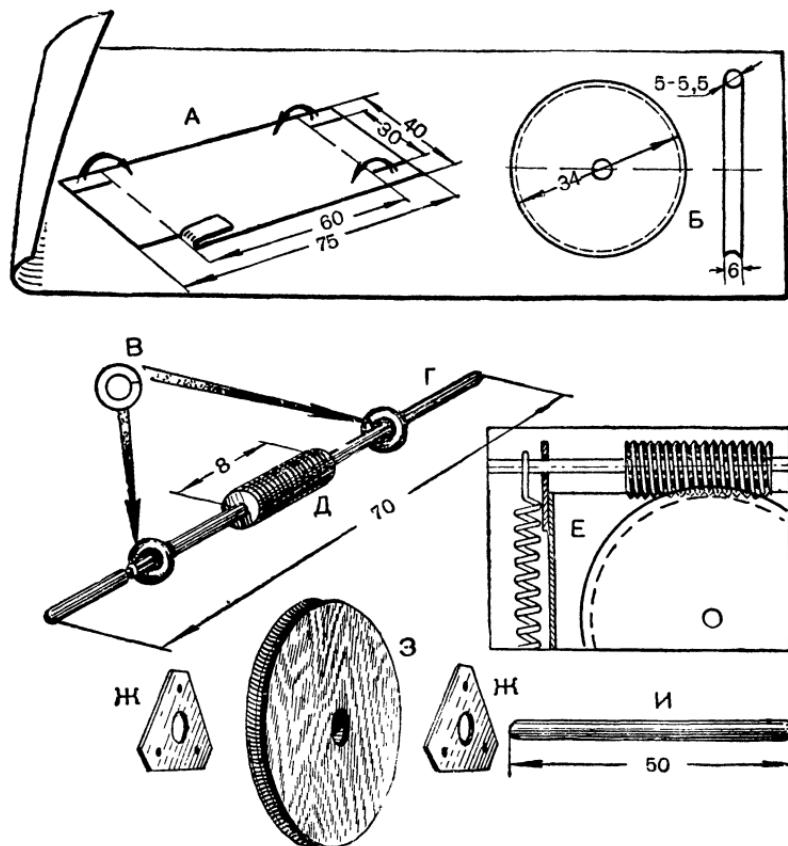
Детали червячного редуктора (рис. 124): А — дно корпуса; Б — заготовка червячного колеса; В — проволочные колечки; Г — вал червяка; Д — червяк; Е — схема сборки; Ж — накладки; З — червячное колесо; И — вал червячного колеса.
